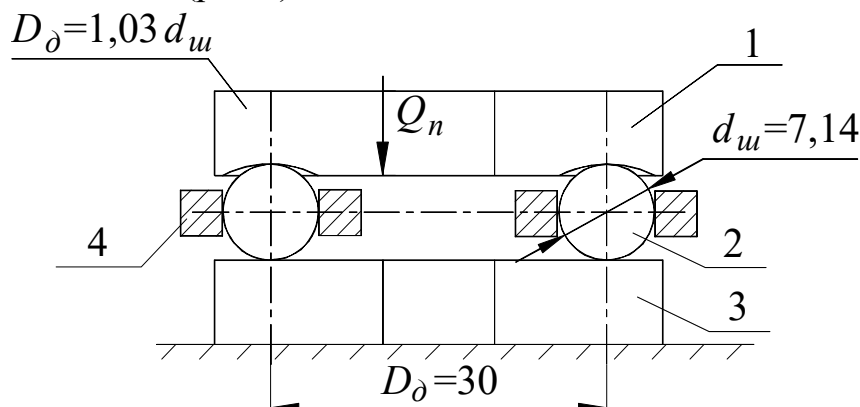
Схема випробувань КП: 1 – верхнє кільце упорного КП; 2 – кульки КП; 3 – випробовуваний плоский кільцевий зразок; 4 –
